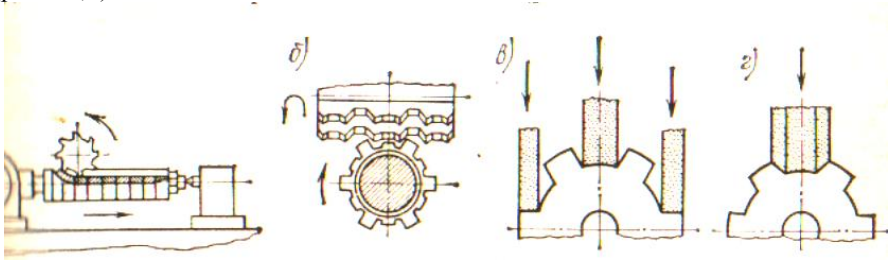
Схема формирования шлицевых валов на горизонтальнофрезерном, б – шлицефрезерном, в - шлицешлифовальном станках
